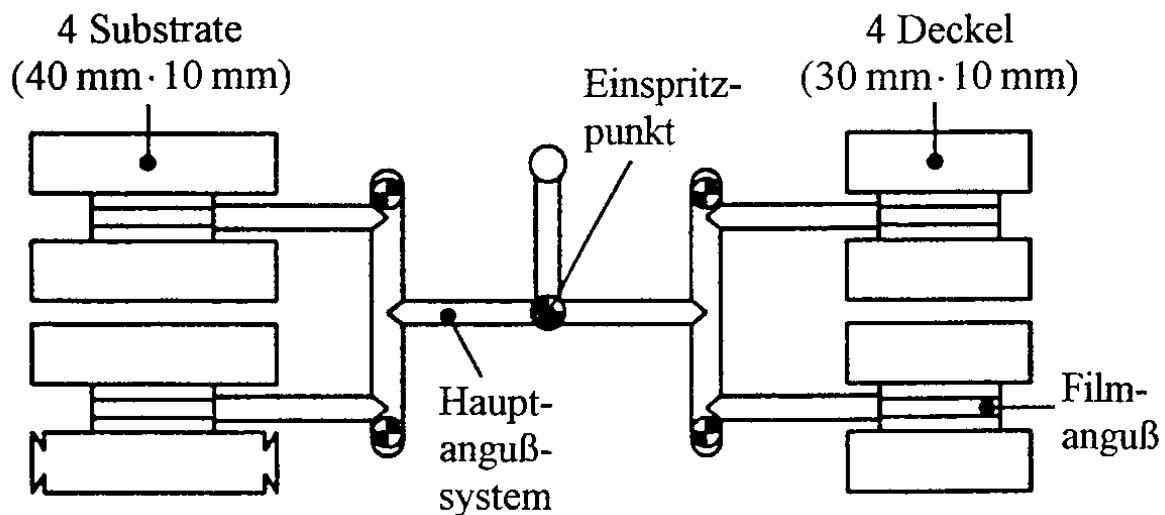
Kavitäten des Spritzgießwerkzeuges
